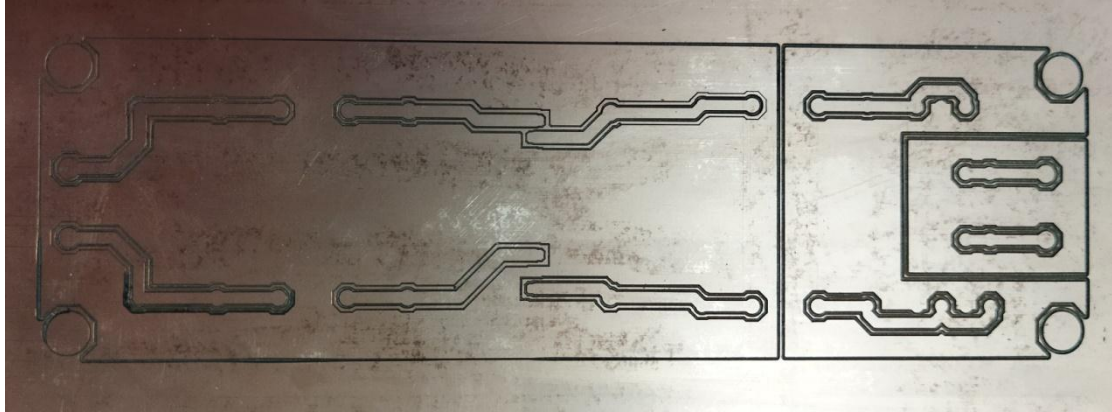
Carte PCB réalisée sur la machine CNC Bungard CCD.
